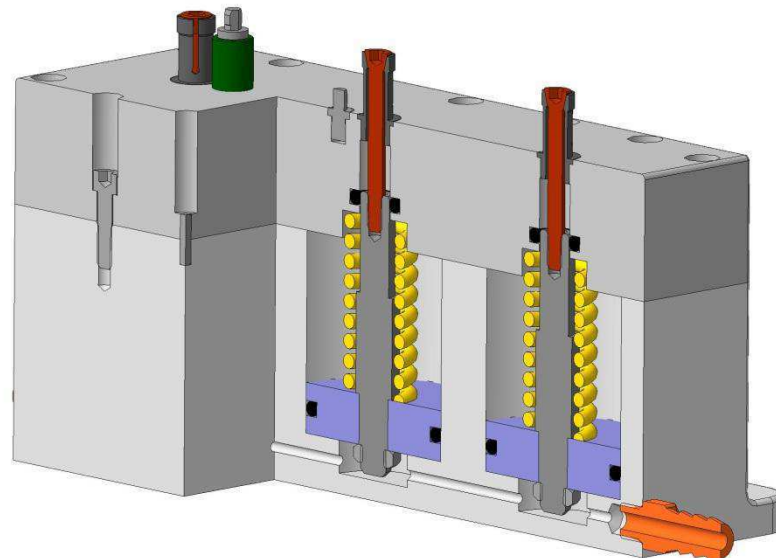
Разрез 3D модели фрезерного приспособления
